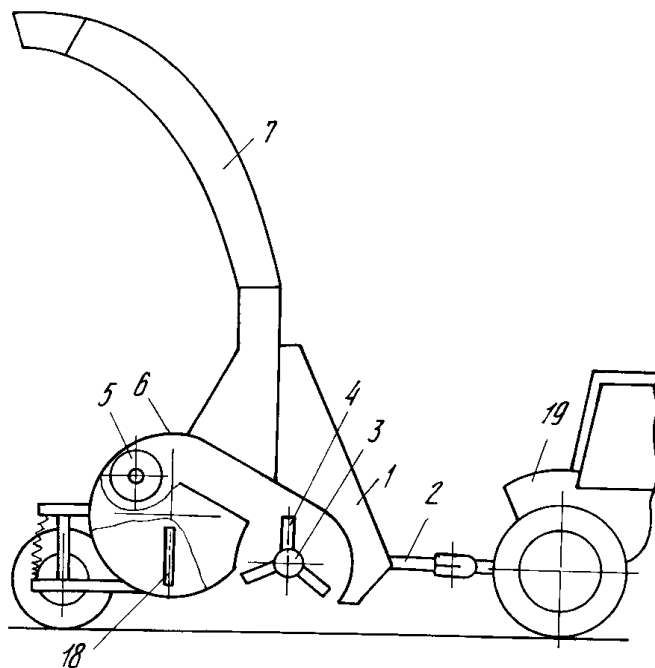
Схема роторной косилки-измельчителя [53]
